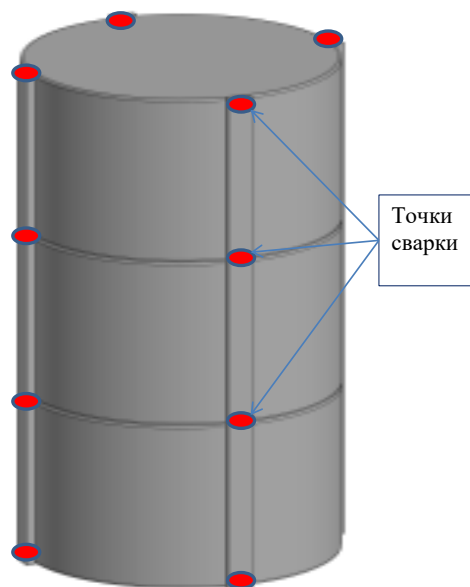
Изготовление переплавляемого электрода путем сварки прессованных цилиндрических брикетов полосками металла (точками показаны места сварки)
